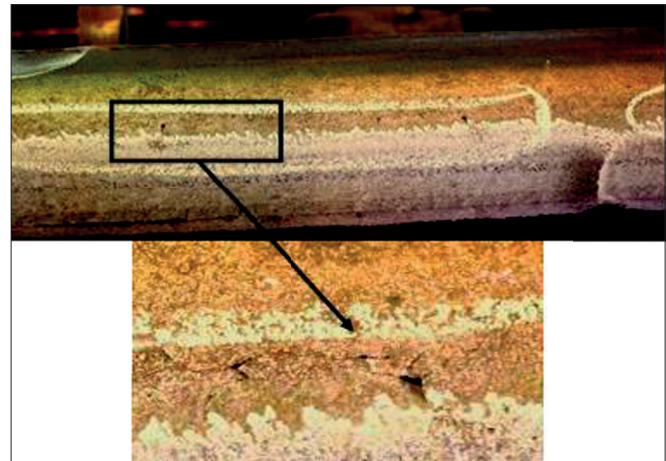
Поверхностный дефект в виде сетчатых трещин на горячекатаной заготовке
